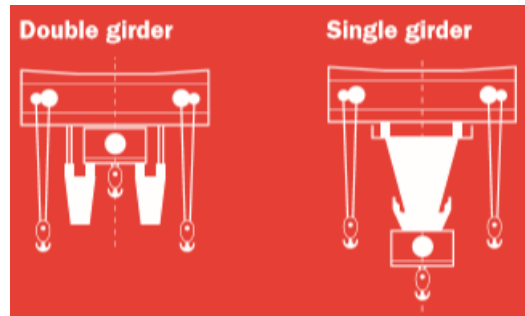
Geometria das secções transversais dupla viga/monoviga[9].
